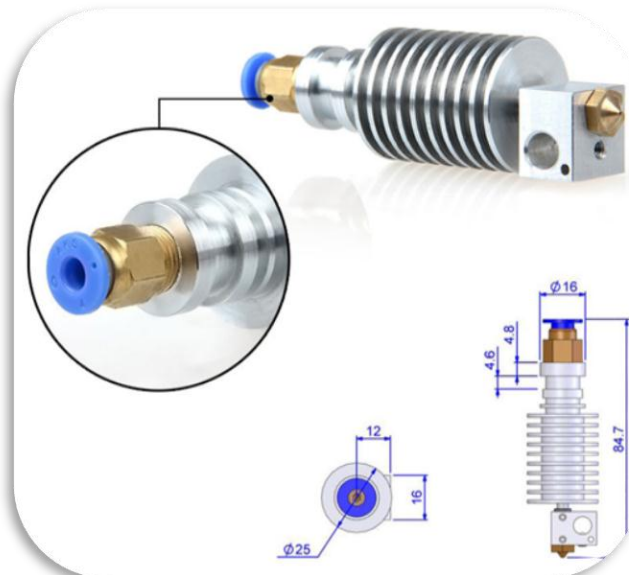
Dimensiones de J-Head, medidas en milímetros.
